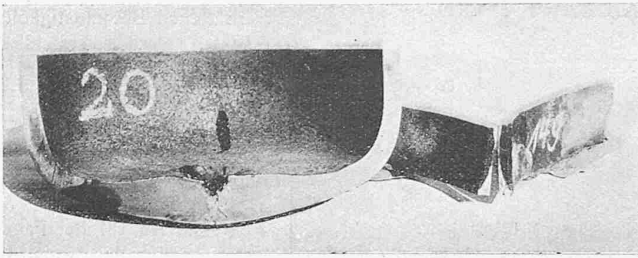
Materialfehler bei nicht explodierten Behältern.
